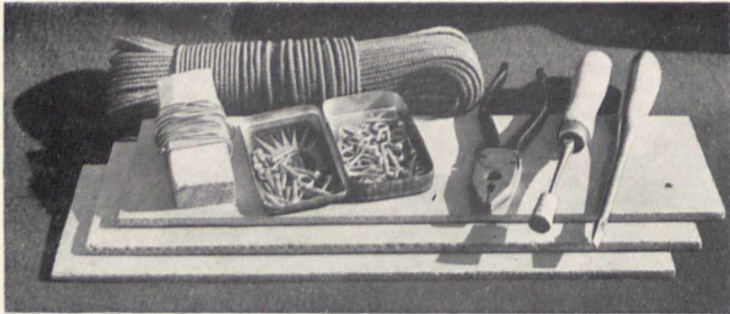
Werkzeug und Material zum Zusammenbau eines Ski-Schlittens
